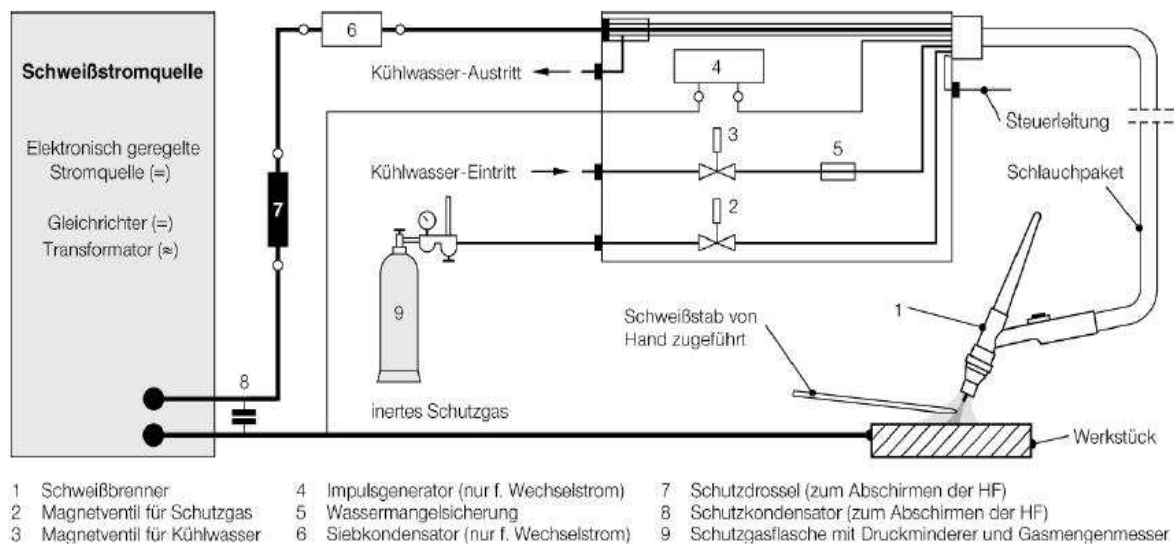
Grundsätzlicher Aufbau einer wassergekühlten WIG-Schweißanlage<sup>[ST03]</sup>
